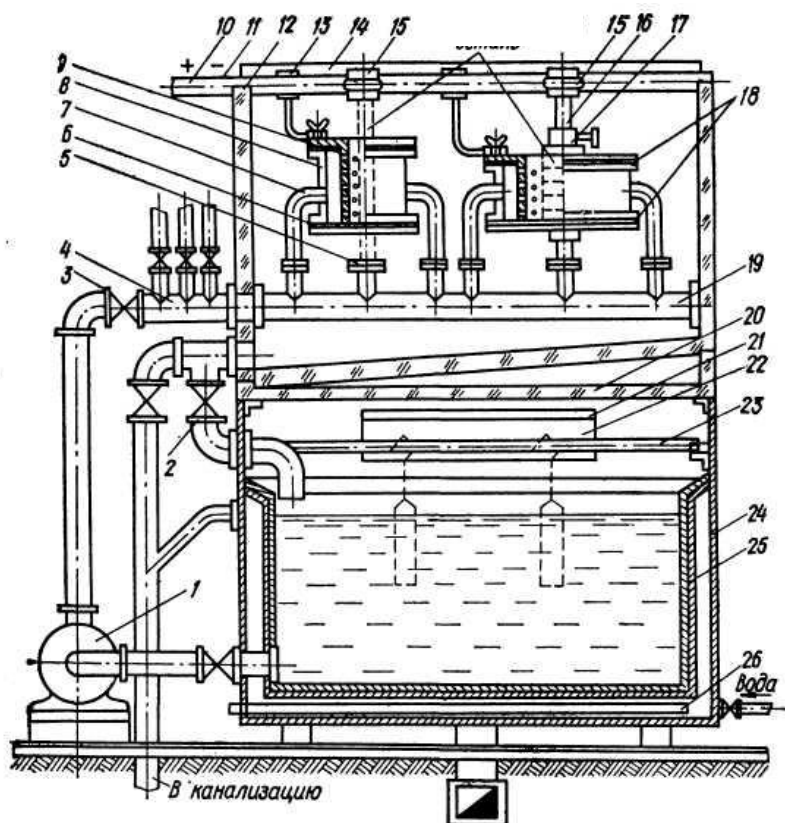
Принципова схема будови установки для реалізації процесу анодно-струминного хромування поверхонь деталей:
